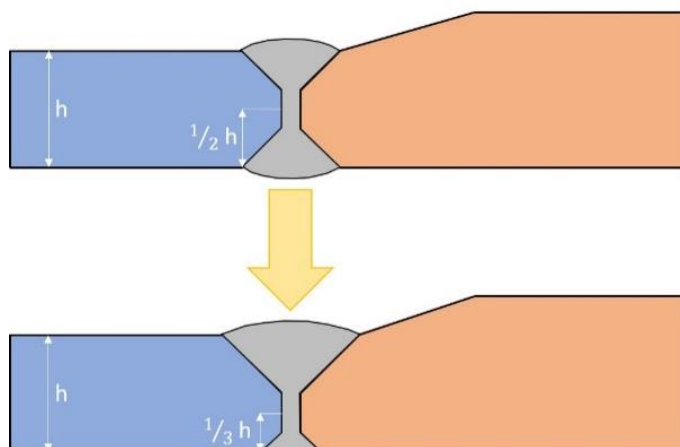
Alteração geométrica da junta de soldadura nos banzos
